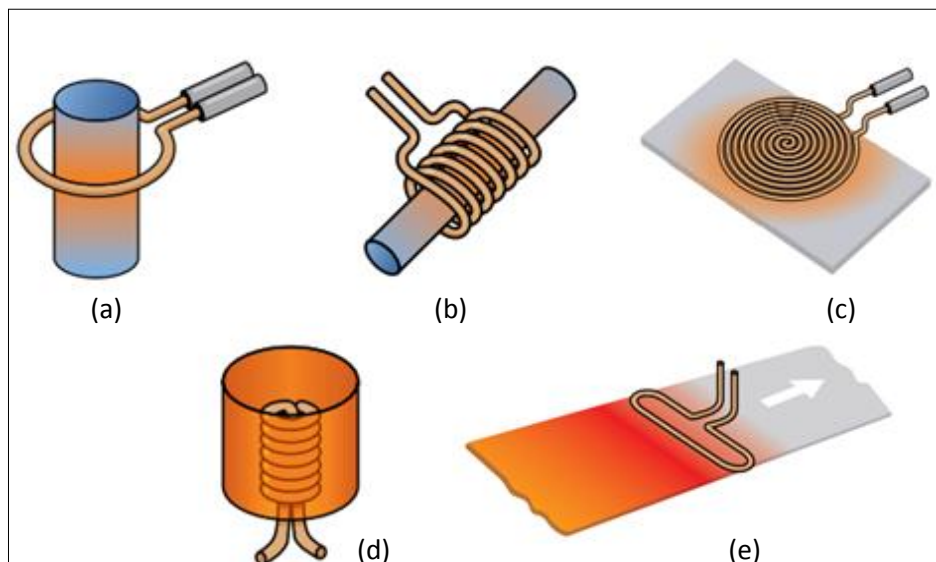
Diversas geometrias de bobinas – (a) bobina de única espira; (b) bobina helicoidal multiespira, (c) bobina de panqueca, (d) bobina interna; (e) bobina de grampo.
